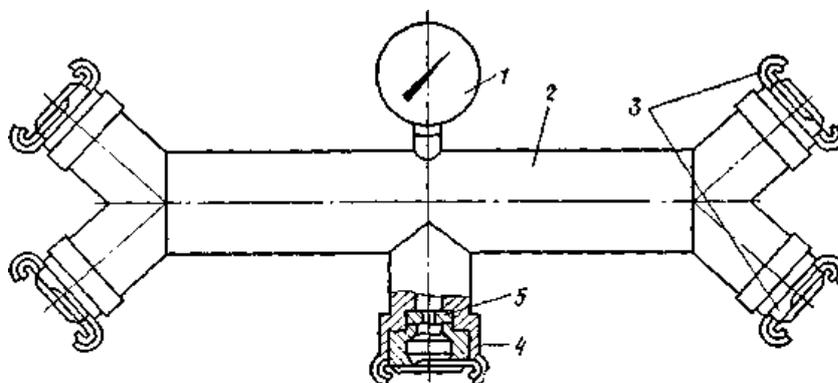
Дозирующая вставка: 1 – манометр; 2 – корпус; 3 – соединительные головки; 4 – приемный патрубок; 5 – дозирующая шайба
